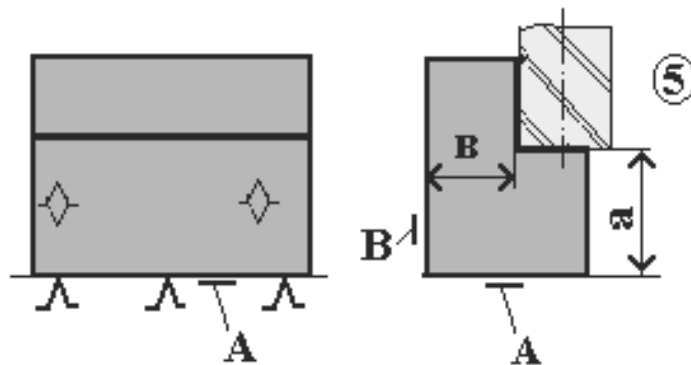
Пример неполной схемы базирования призматической заготовки.
